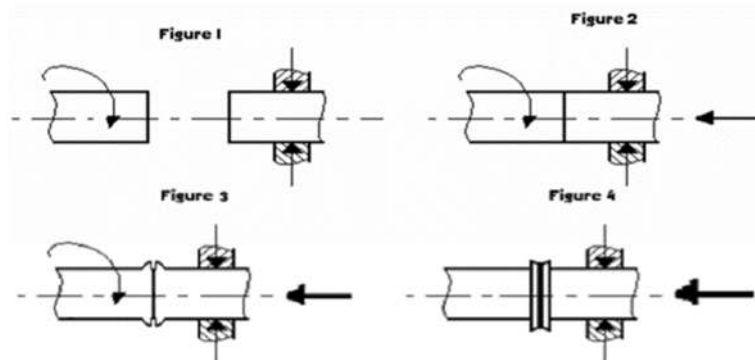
6: Différentes étapes du soudage par friction
